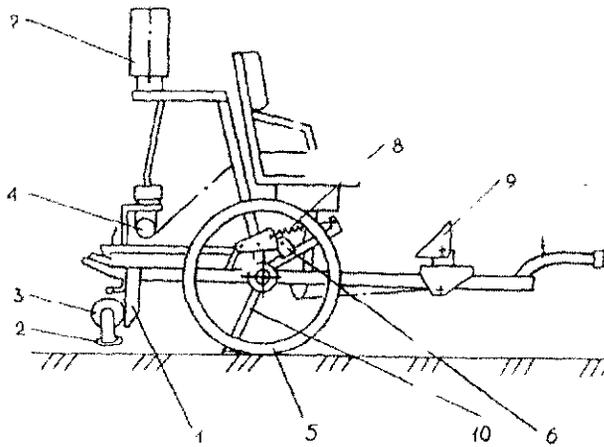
Схема устройства для контактного нанесения гербицида: 1 - рама; 2 - поддон; 3 - валец; 4 - поплавковая камера; 5 - колесо опорное; 6 - палец; 7 - бак; 8 - компенсатор; 9 - педаль установки высоты пальца; 10 - лапа опорная.
